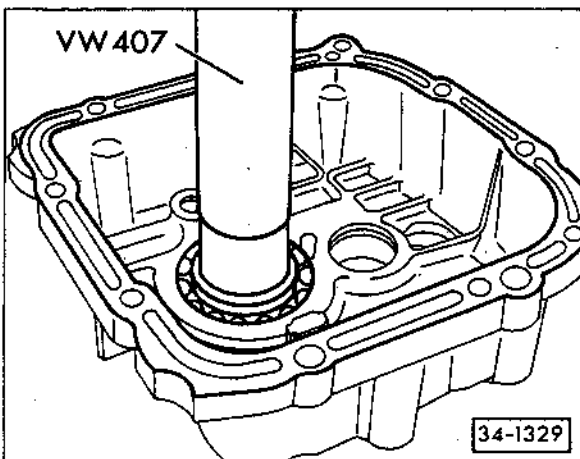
Rillenkugellager aus Lagerschild auspressen
